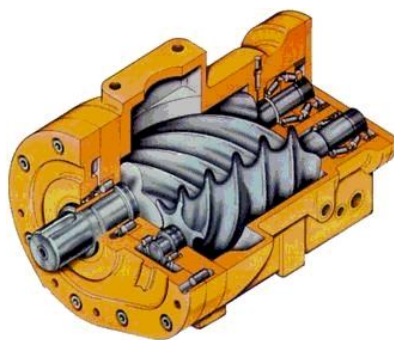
Сжимающий элемент винтового компрессора в разрезе
